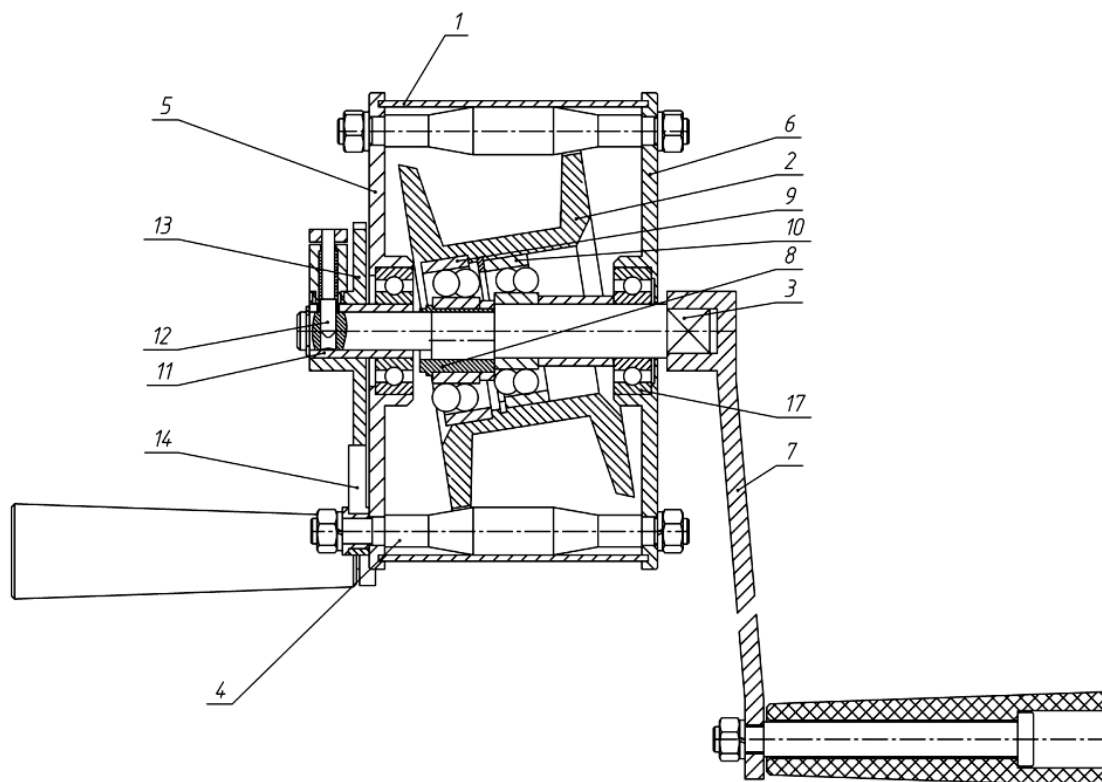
Конструкция РПТМ со сферическими подшипниками для аварийно-спасательного устройства: 1 – защитная крышка корпуса; 2 – барабан; 3 – приводной вал; 4 – конические ролики; 5,6 – крышки корпуса; 7 – рукоятка; 8 – эксцентриковая втулка; 9,10 – сферические подшипники; 11 – втулка; 12 – стопорный стержень; 13 – храповое зубчатое колесо; 14 – собачка; 15 – подшипник
